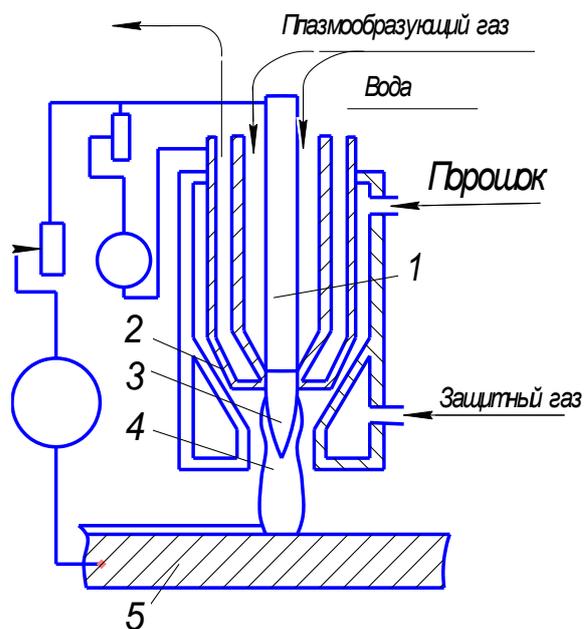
Схема плазменной наплавки с вдуванием порошка в дугу
